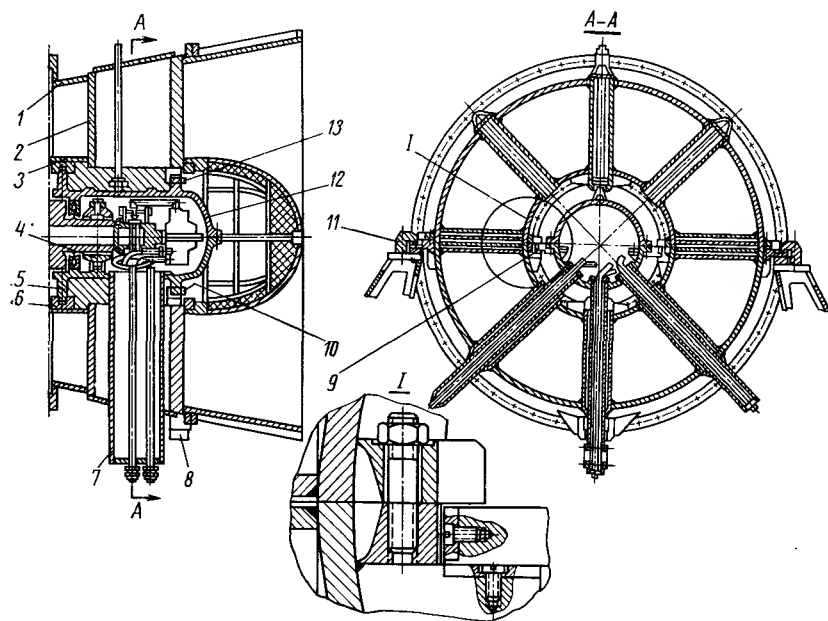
Крепление корпуса подшипника ГТУ мощностью 50 000 квт:
